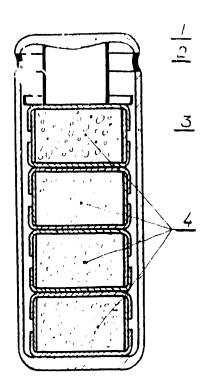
Рис. I. Разрез герметичного блочка. (І-крышка, 2-место сварки крышки с корпусом, 3-корпус, 4-пеналы с облучаемым мате риалом)
